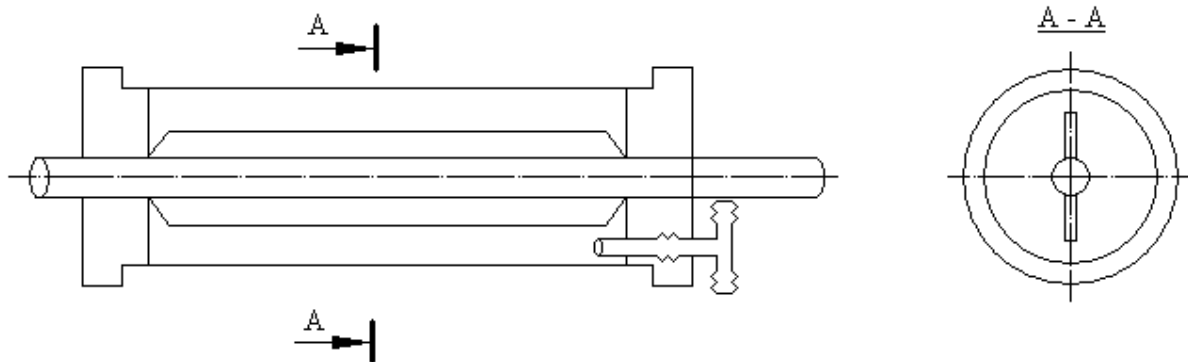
Прямоточный солнечный трубчатый вакуумированный коллектор.
